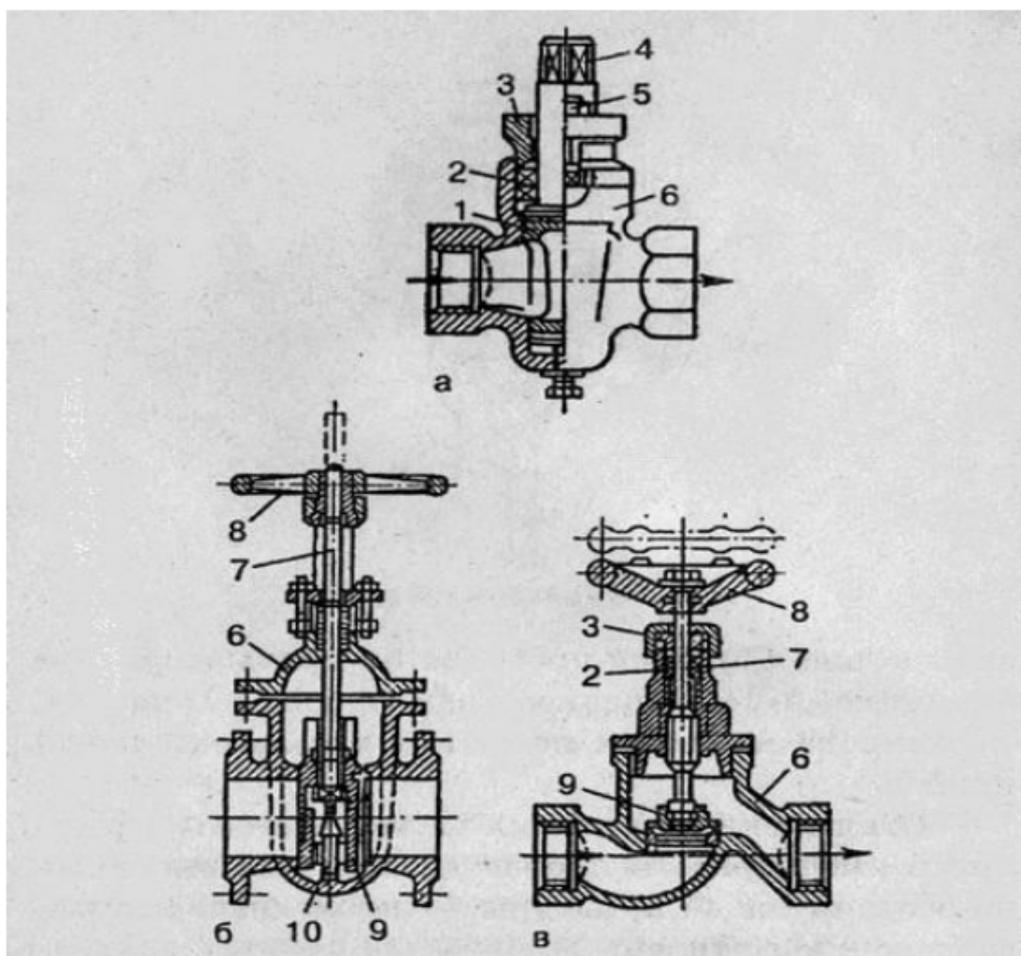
Арматура систем отопления: а — пробковый кран; б — задвижка; в — регулирующий кран: 1 — пробка; 2 — сальник; 3 — вкладыш сальниковый; 4 — четырехгранный торец пробки; 5 — болт; 6 — корпус; 7 — шпindel; 8 — маховик; 9 — диски затвора; 10 — клин
